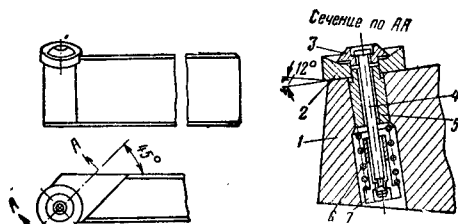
Режущая часть чашечных резцов для обработки бандажей
